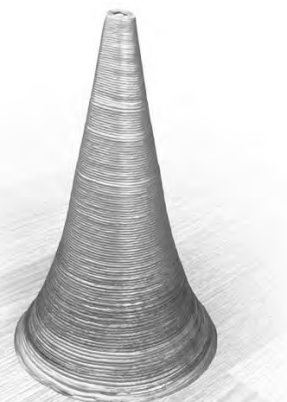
Внешний корпус элемента, полученного аддитивной наплавкой
